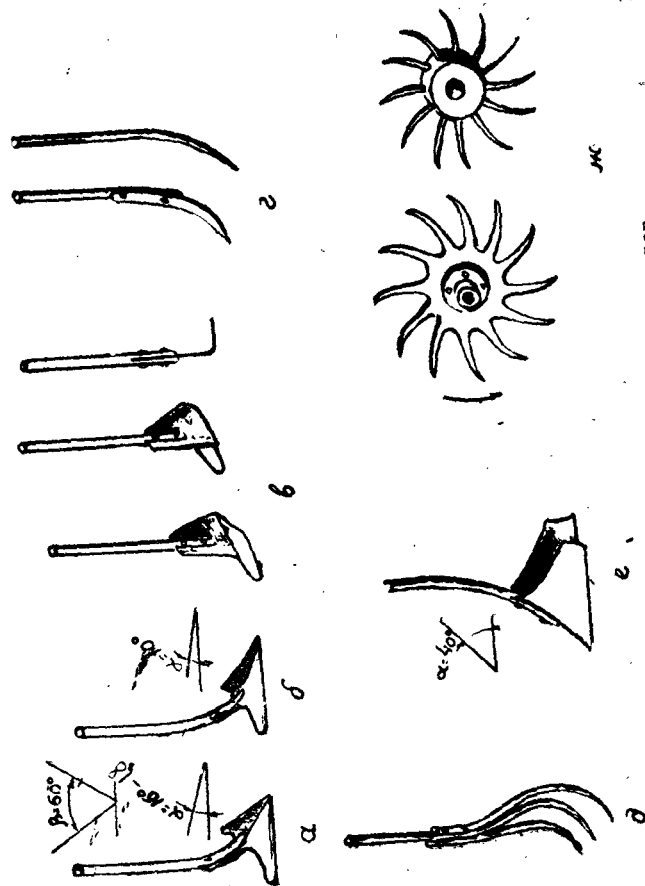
Рабочие органы культиваторов. а — универсальная полевая лапа; б — плоскорезная полевая лапа; в — полевые орывки; г — долоты для глубокого рыхления почвы; д — зубовой рыхлитель; е — окучник; ж — игольчатый ротационный рыхлитель.
